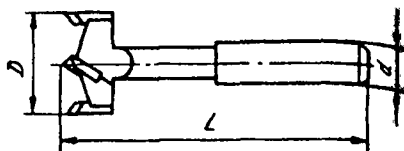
Сверло чашечное с твердосплавными пластинами, длинные
